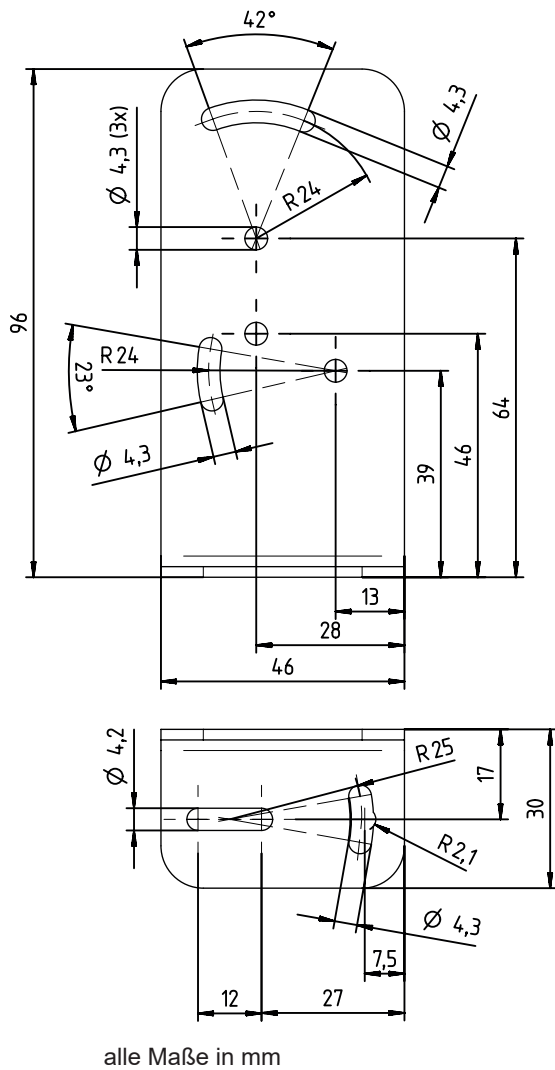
Maßzeichnung Befestigungswinkel BT 300M.5
